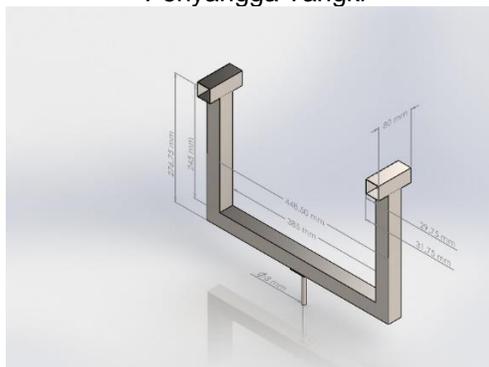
Alternatif 2 Desain Penyangga Spakbor
